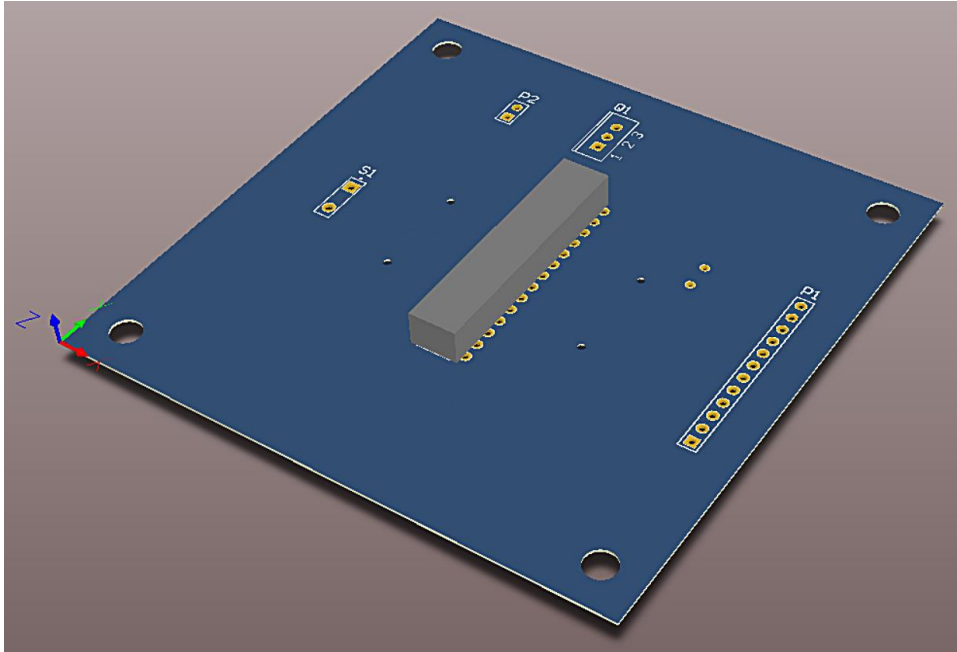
Diseño PCB subsistema de comunicaciones, Bottom Plate.
